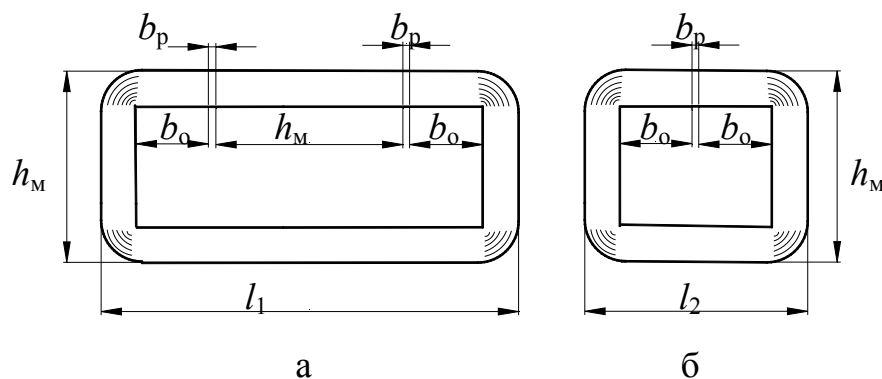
Віті заготовки (а, б) для виготовлення планарного стикового трифазного магнітопроводу зі зниженою металомісткістю: 1 – стрижень; 2 – ярмо; 3 – котушка обмотки.
